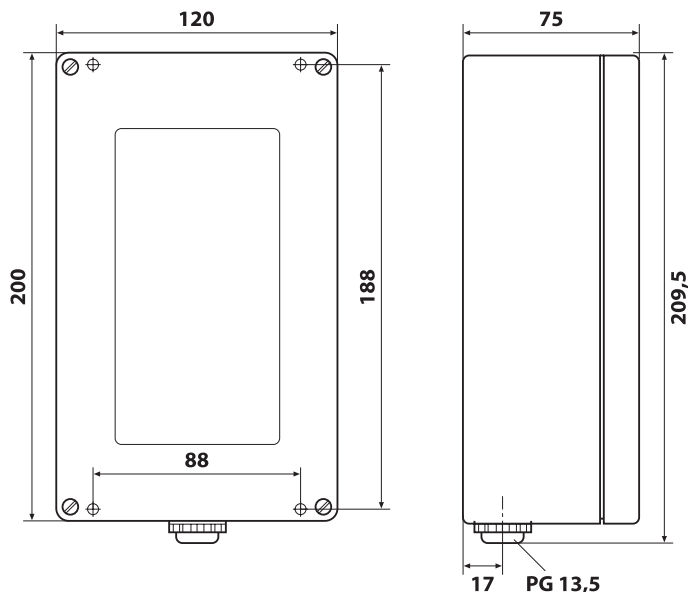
Aparato MK2430 en carcasa de montaje sobre pared
